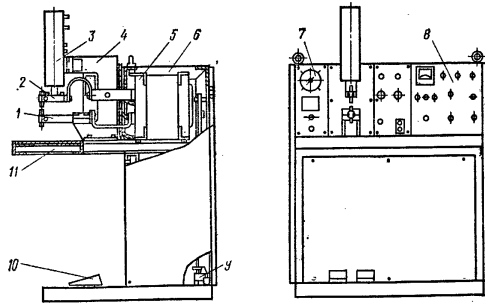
Машина МТК-1601 конденсаторная для точечной сварки
